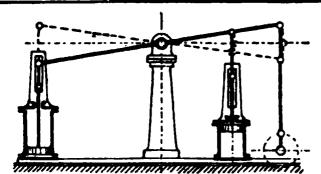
Woolfsche Balanciermaschine mit entgegengesetzt gerichtetem Kolbenlauf, System Mac Naught.
